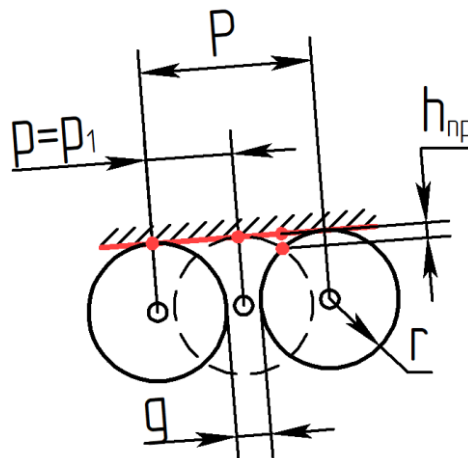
Схема расположения СМП на прямолинейной поверхности профиля обрабатываемой детали.
